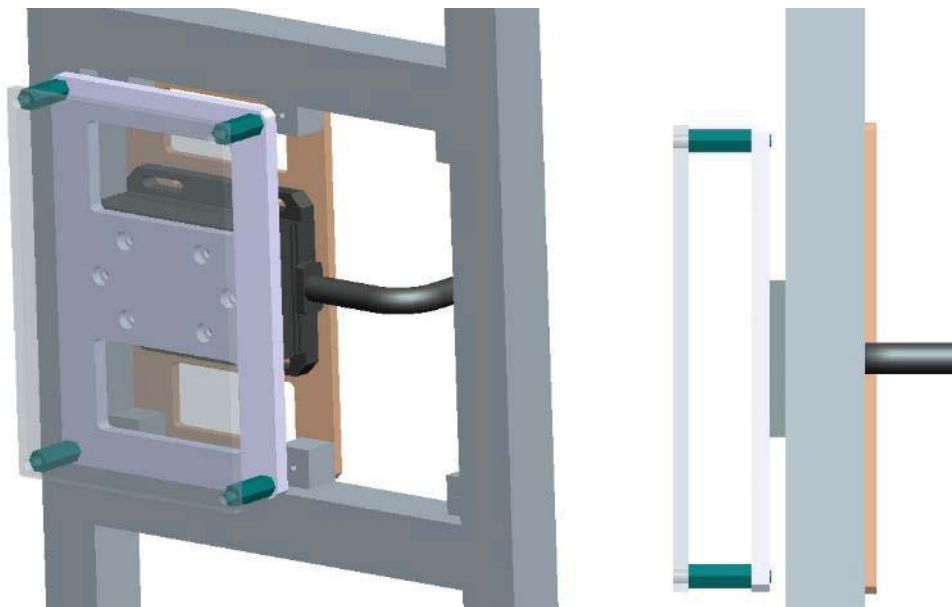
Imágenes CAD del montaje experimental de la mesa dinamométrica, portaprobetas y probeta a remachas.
